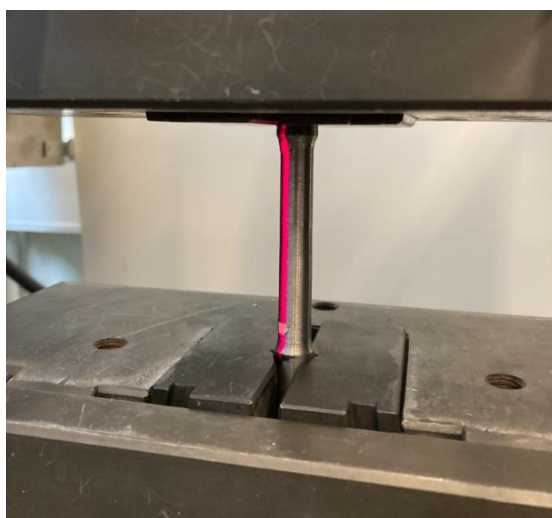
Hotové zkušební vzorky pro tahovou zkoušku
